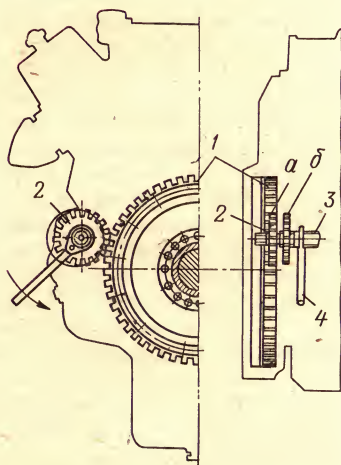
Механизм проворота коленчатого вала двигателя ЯМЗ-240Б;
